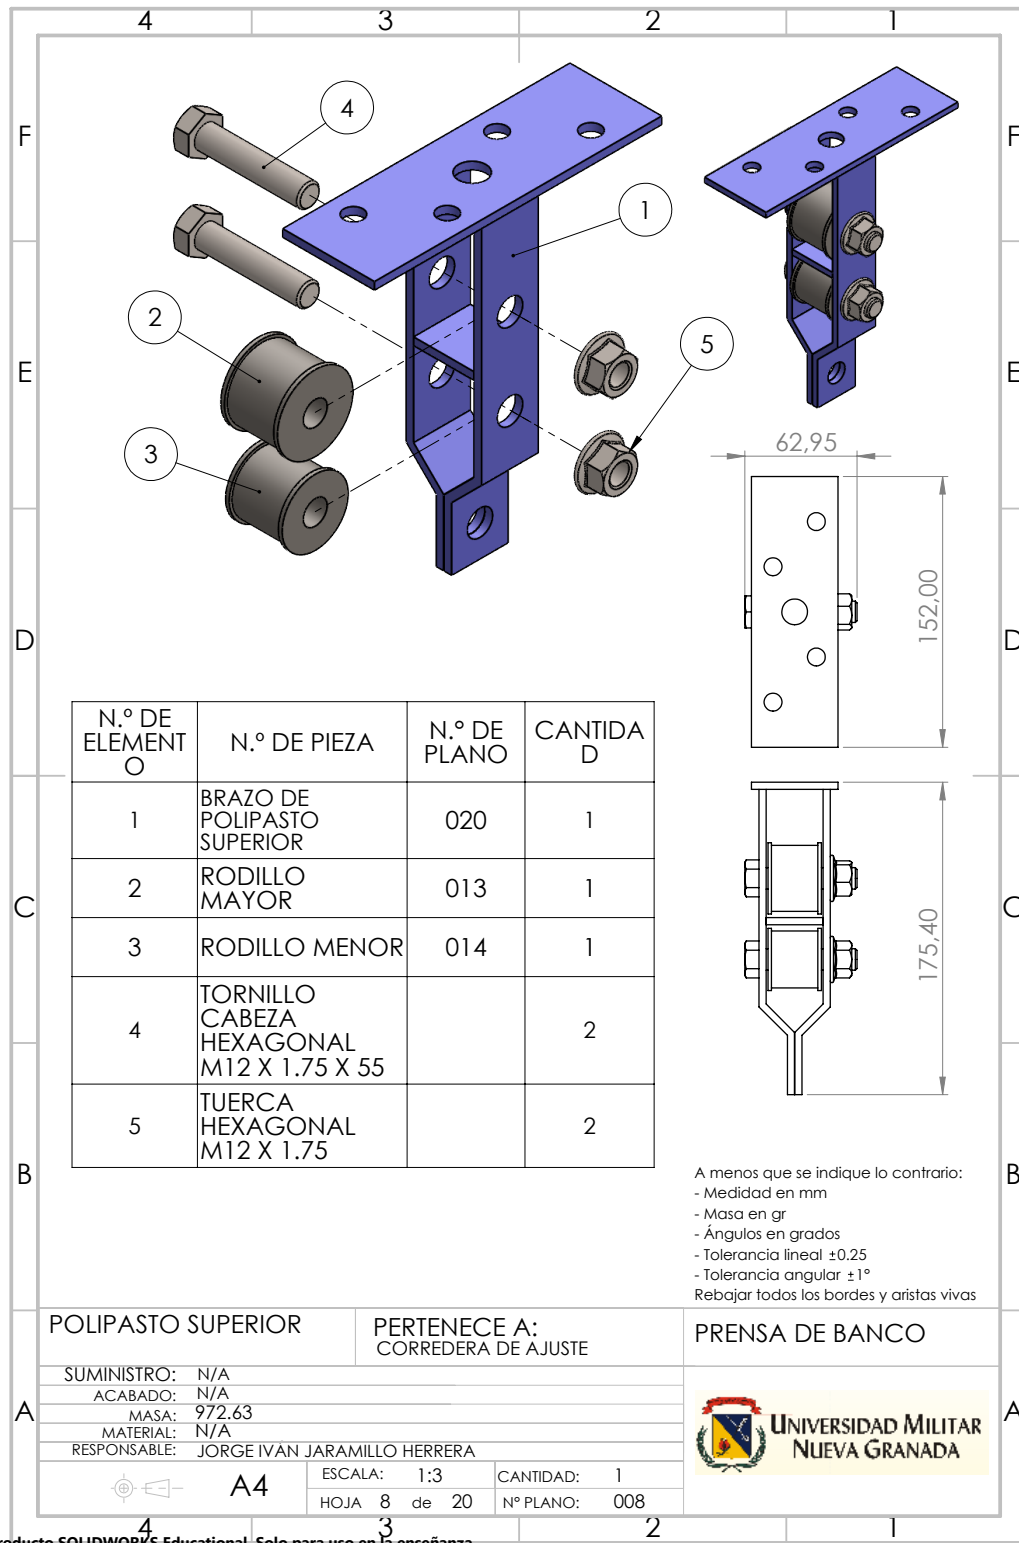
Plano 008, del ensamble "Polipasto Superior". Modelo CAD y plano elaborado por el autor mediante la herramienta de ensamble y dibujo de "Solidworks".
